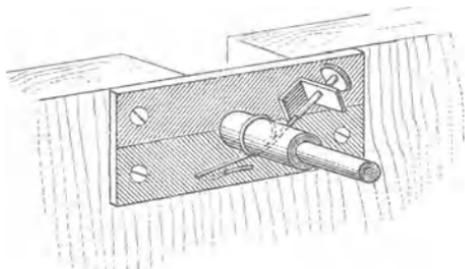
Dieselbe Bremsvorrichtung in Ansicht bei Muffenführung.
